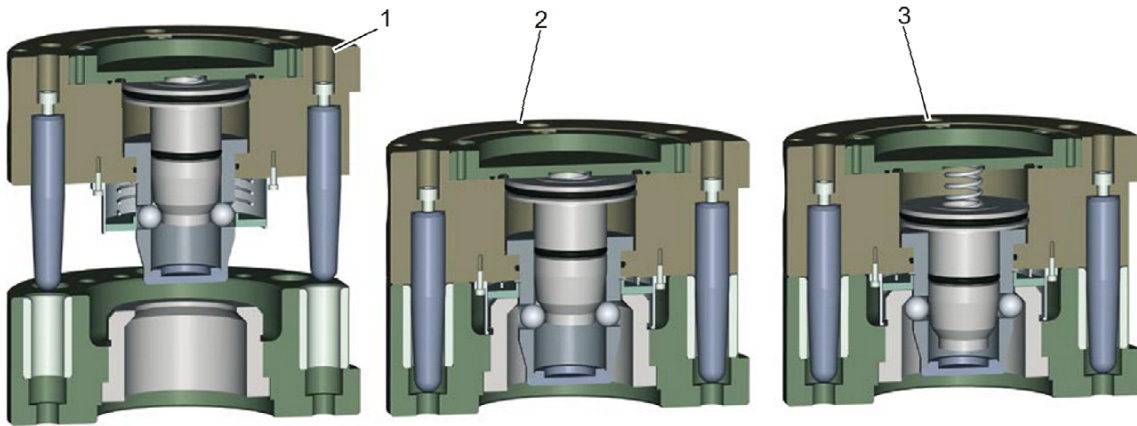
Schnittbild zum Verriegelungsvorgang beim Werkzeugwechsler (WZW). Im Zustand 1 ist der obere, roboterseitige WZW noch nicht in den unteren, werkzeugseitigen WZW eingetaucht. Im Zustand 2 sind die WZW in der Verriegelungsposition. Zustand 3 zeigt den verriegelten Zustand. Der innere Stößel wird per Druckluft und durch die Feder im roboterseitigen WZW nach unten gedrückt und schiebt die Kugeln seitlich in den Kranz des werkstückseitigen WZW. Bild aus [IPR11].
